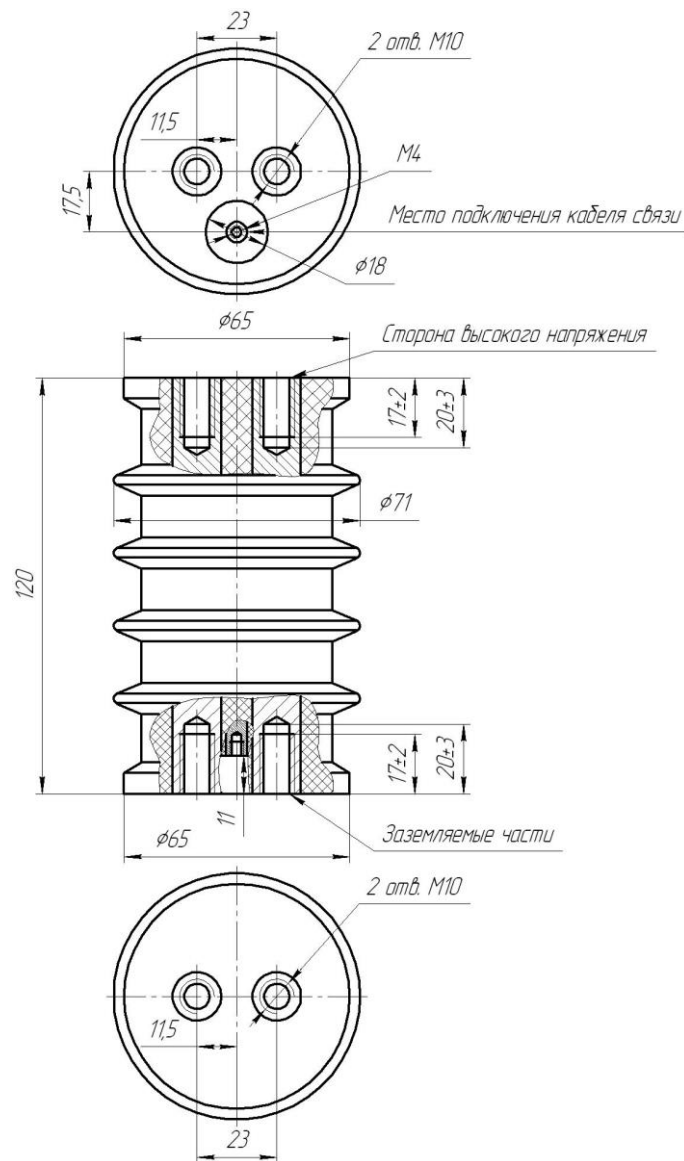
Габаритные, установочные и присоединительные размеры измерительного компонента устройства I-TOR-6(10)-U, конструктивное исполнение – опорное.
